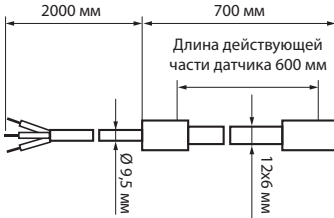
Габариты датчика кровли DEVI Roof 850R
